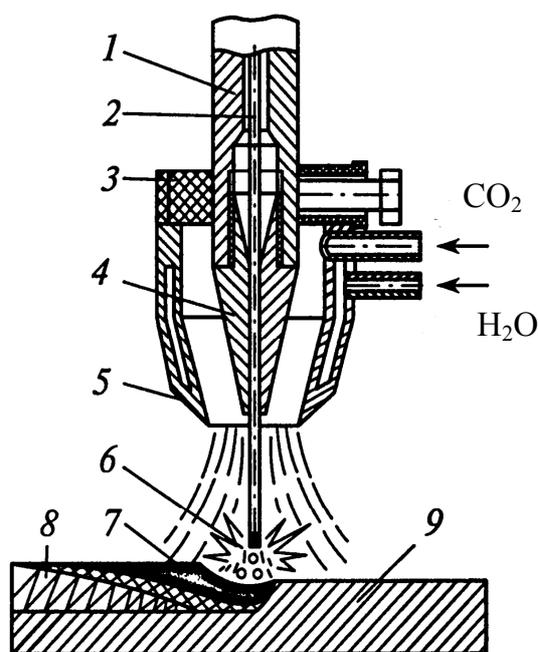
Схема наплавки в среде углекислого газа: 1 – мундштук; 2 – электродная проволока; 3 – горелка; 4 – наконечник; 5 – сопло горелки; 6 – электрическая дуга; 7 – сварочная ванна; 8 – наплавленный металл; 9 – наплавляемая деталь
